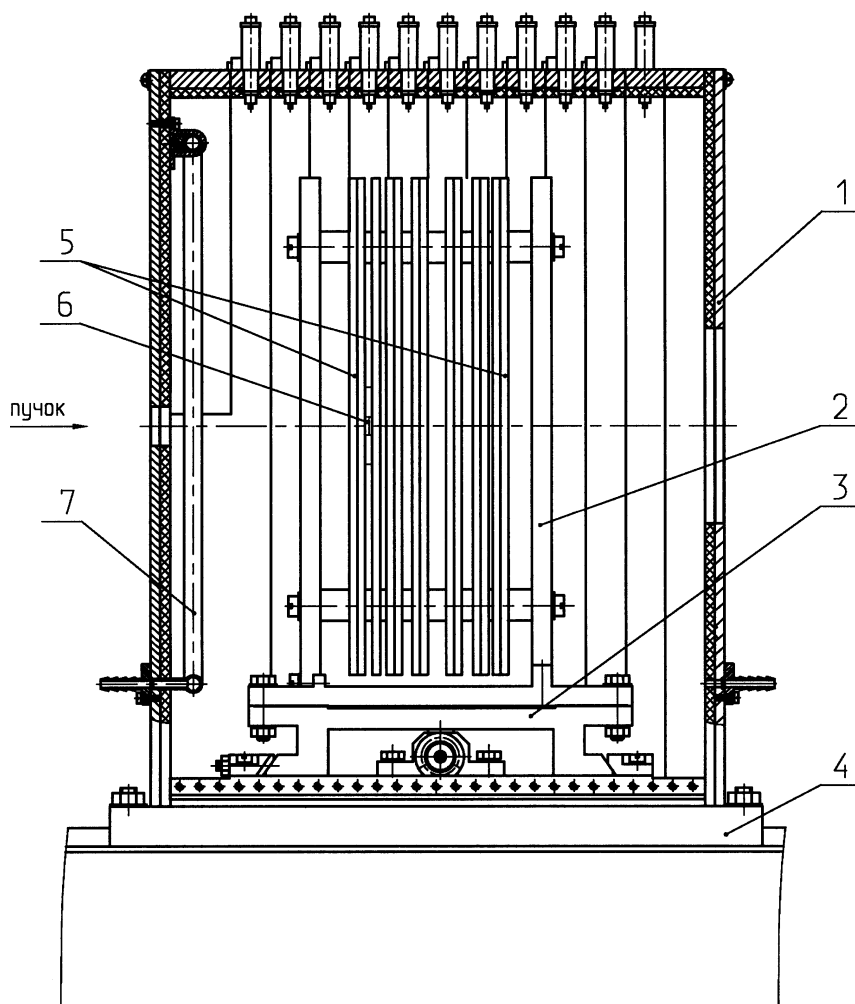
Комбинированный блок ПВД (чертеж в продольном разрезе): 1 – задняя стенка алюминиевого кожуха; 2 – задняя несущая стойка; 3 – каретка поперечного перемещения; 4 – каретка продольного перемещения; 5 – диски с МКД; 6 – АМ, закрепленная на D3; 7 – трубка для поддува холодного азота.
